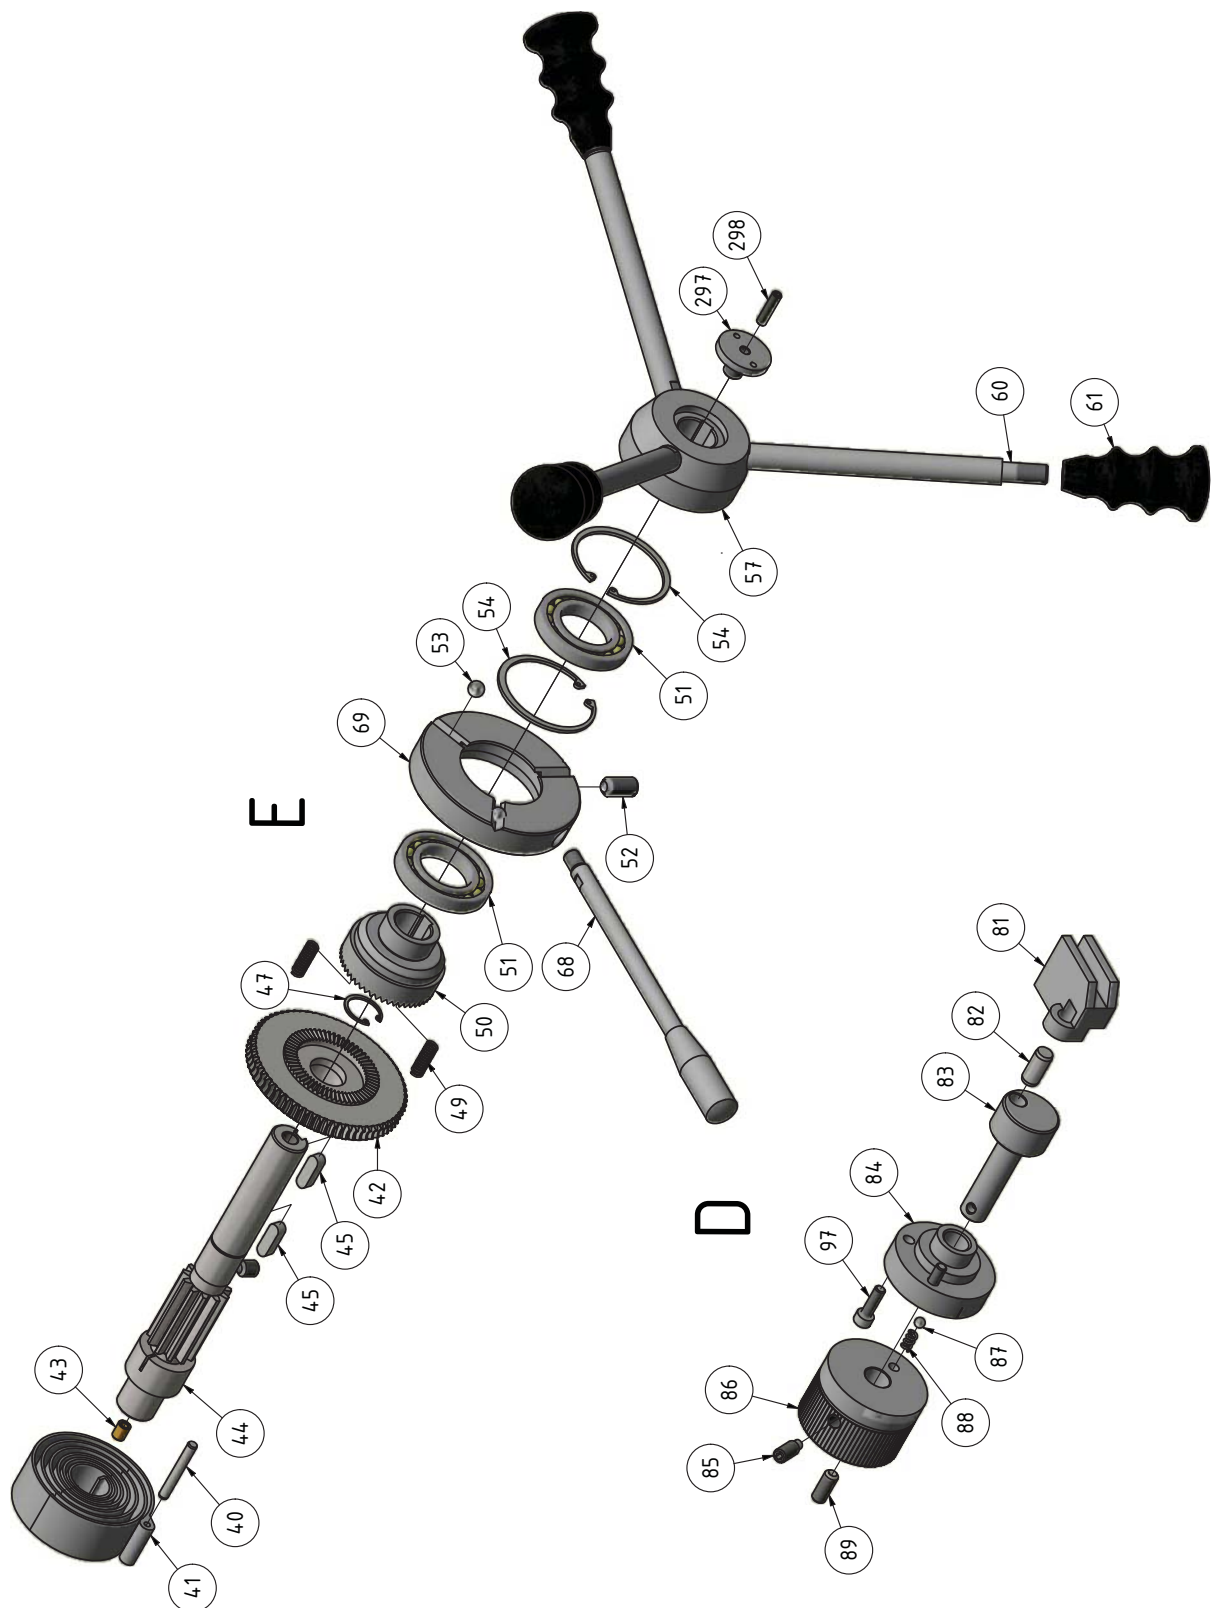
Vorschubgetriebe 2 von 4 - Feed gear box 2 of 4
